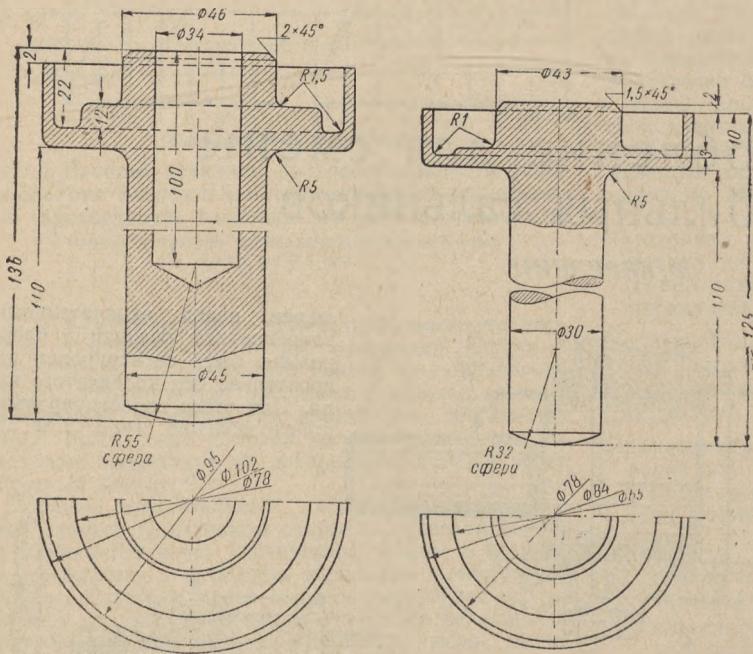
Оправка для запрессовки сальника ступицы заднего колеса автомобиля „Победа“.
